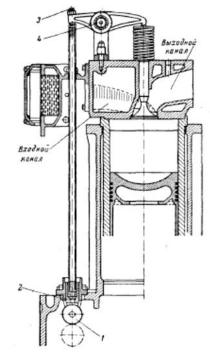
Привод клапанов 1-ролик толкателя, 2-толкатель штанги, 3 — регулировочный винт, 4 - коромысло
